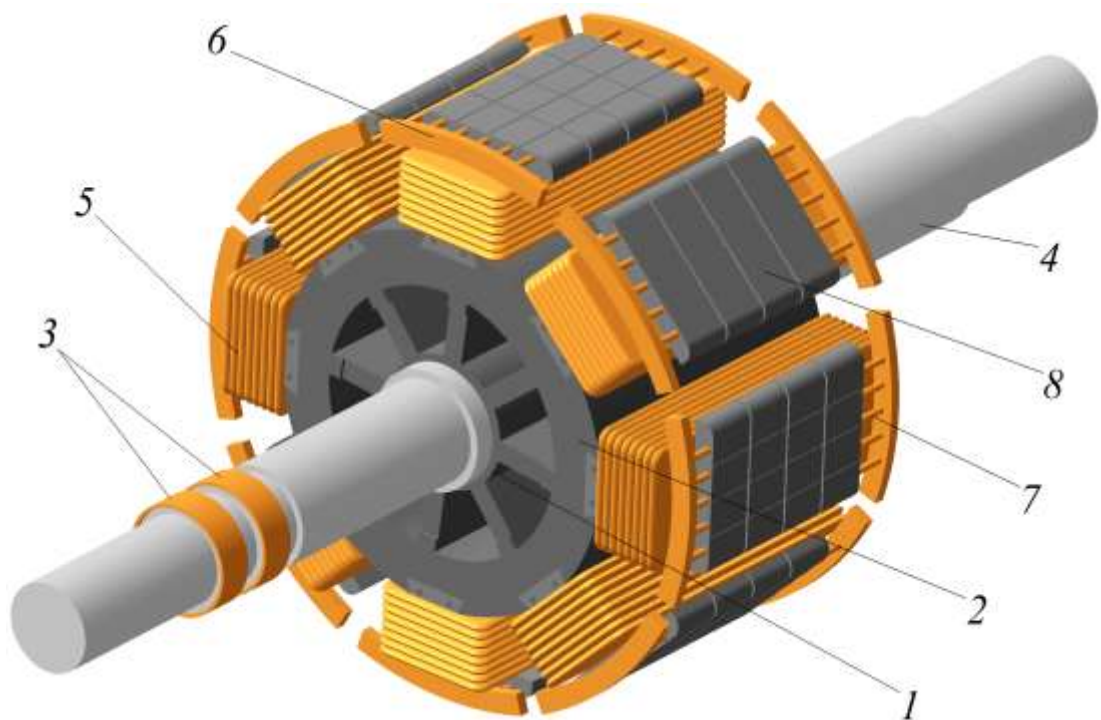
Конструкція явнополюсного ротора: 1 – основа ротора; 2 – обід ротора; 3 – контактні кільця; 4 – вал; 5 – котушка обмотки збудження; 6 – сегмент демпферної обмотки; 7 – стрижень демпферної обмотки; 8 – осердя полюса
